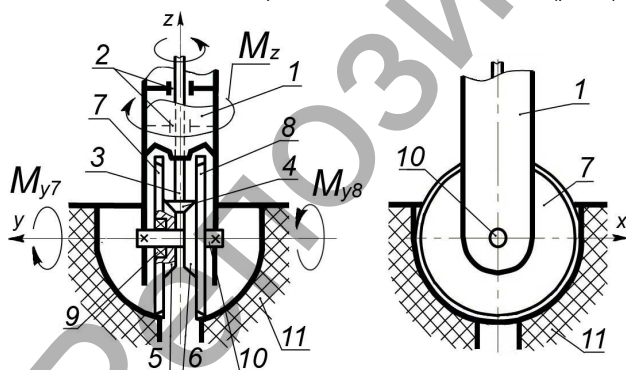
Конструкция устройства для обработки отверстий в изделиях из ПКМ
